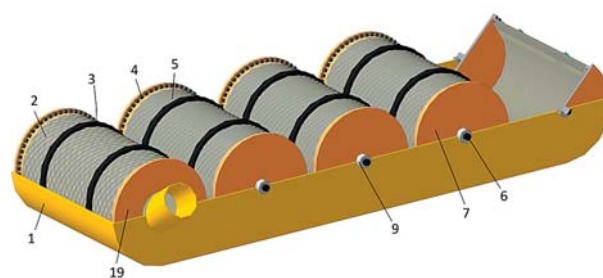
Установка с цилиндрическими барабанами-резонаторами из витков безосевого шнека в виде лезвия ножа
